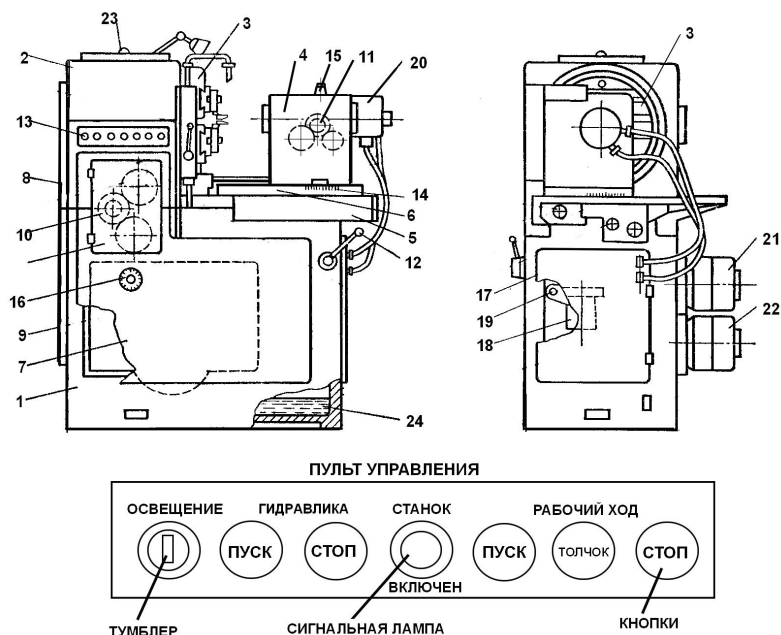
Внешний вид станка: 1 – станина; 2 – стойка; 3 – люлька с суппортами; 4 – бабка изделия; 5 – стол; 6 – поворотная плита; 7 – реверсивный механизм (под крышкой); 8 – крышка гитары скоростей (главного движения); 9 – крышка гитары привода подачи; 10 – гитара обката; 11 – гитара деления; 12 – рукоятка ускоренного перемещения стола и зажима; 13 – кнопочный пульт управления; 14 – шкала расстояний от торца шпинделя до геометрического центра станка; 15 – лимб вертикального смещения шпинделя; 16 – счетчик циклов; 17 – лимб установки механизма врезания; 18 – распределвал; 19 – четырехгранный конец вала червяка привода распределвала; 20 – гидроцилиндр механизма зажима заготовки; 21 – электродвигатель привода кинематики станка; 22 – электродвигатель привода гидронасоса; 23 – указатель смазки; 24 – резервуар масла
